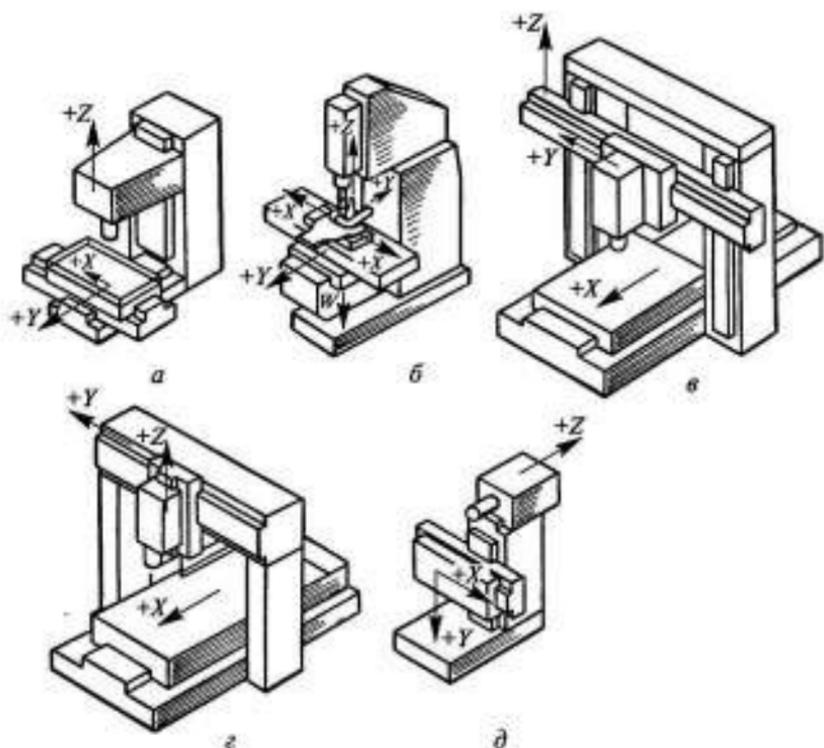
Компоновки фрезерных станков с ЧПУ с обозначением осей координат X , Y , Z и W :
